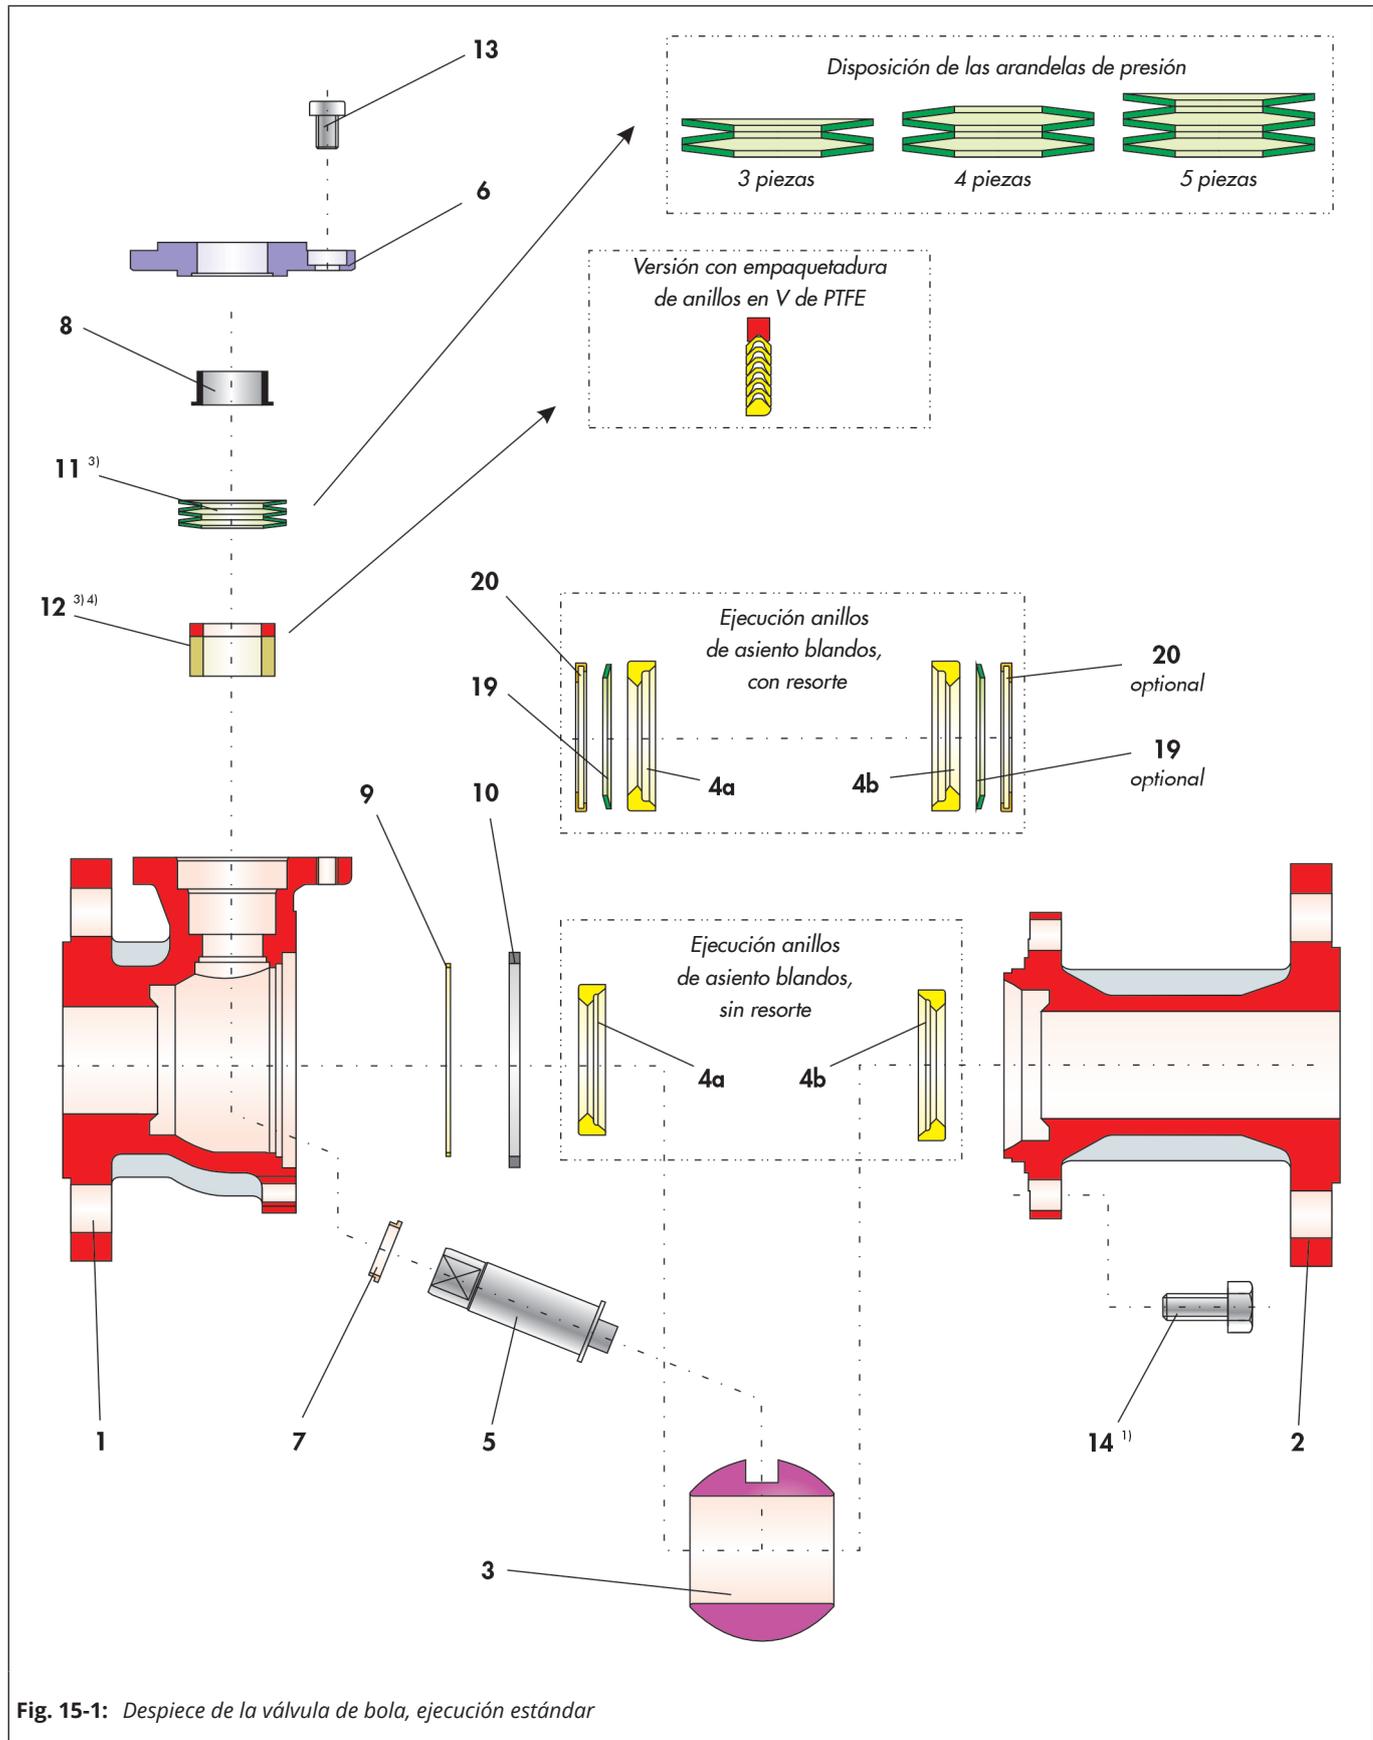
Despiece de la válvula de bola, ejecución estándar
